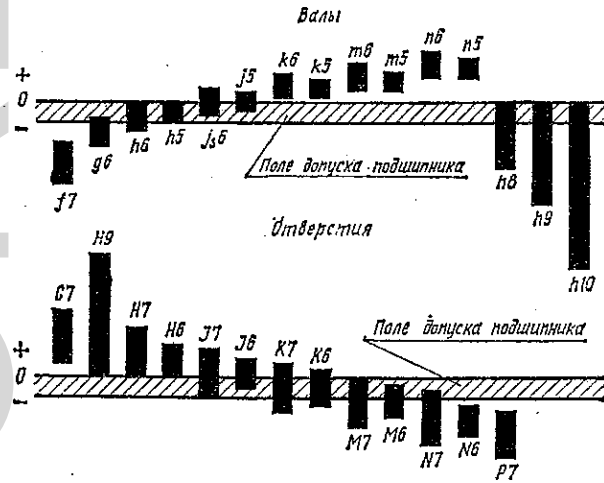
Схема расположения полей допусков валов и отверстий для различных посадок
